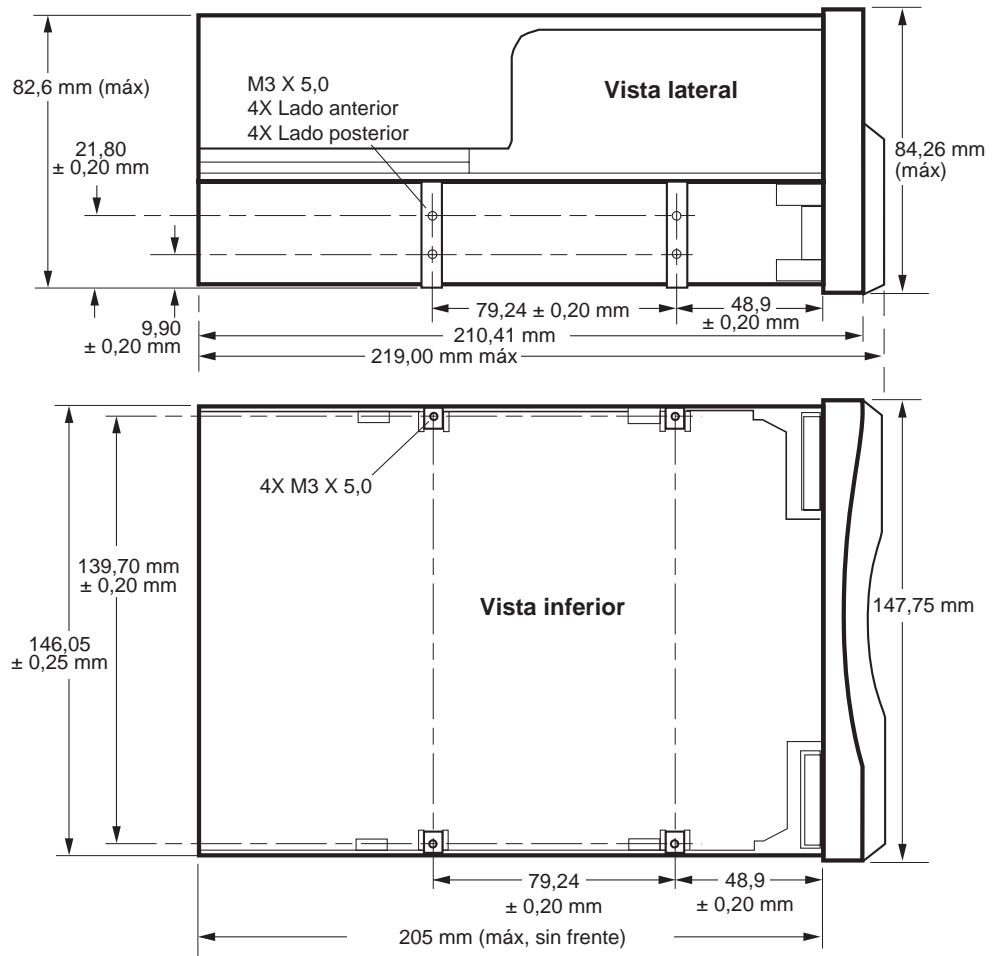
Unidad Viper HVD/LVD Interna: dimensiones
